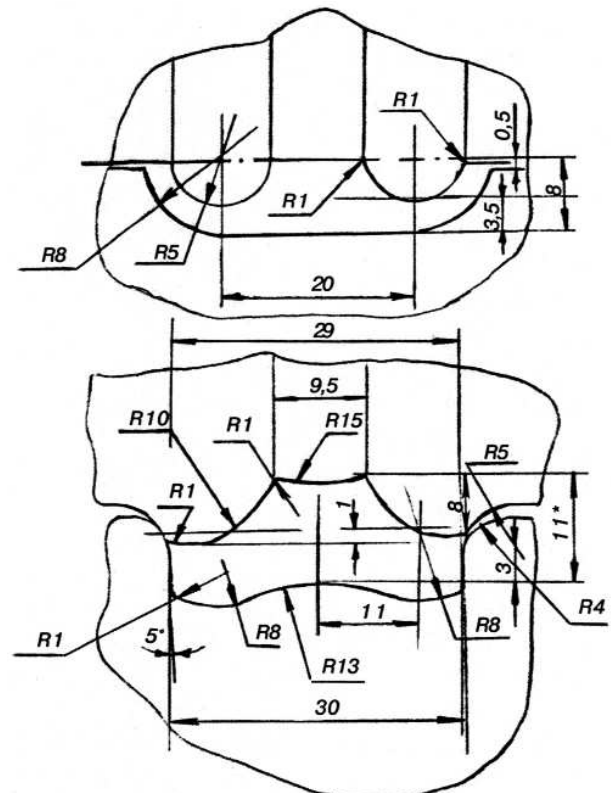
Двухпереходная калибровка для изготовления колодки парной 8-8-ОСТ 1.11554-74
